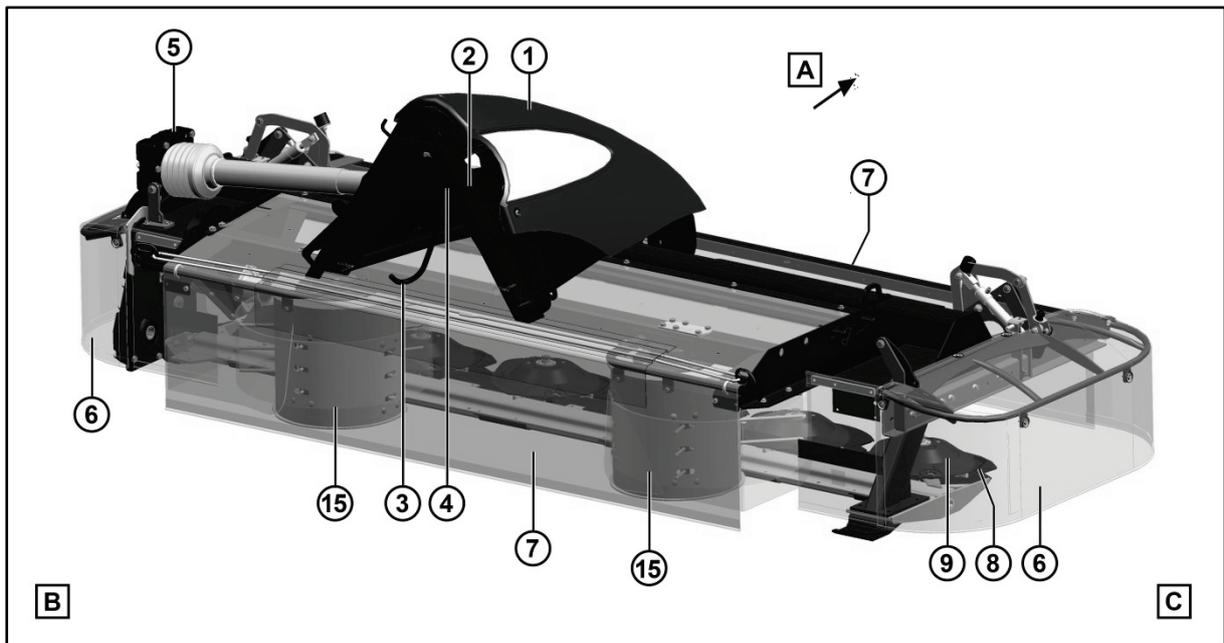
Componentes de la máquina SM 3060 FP-SL
